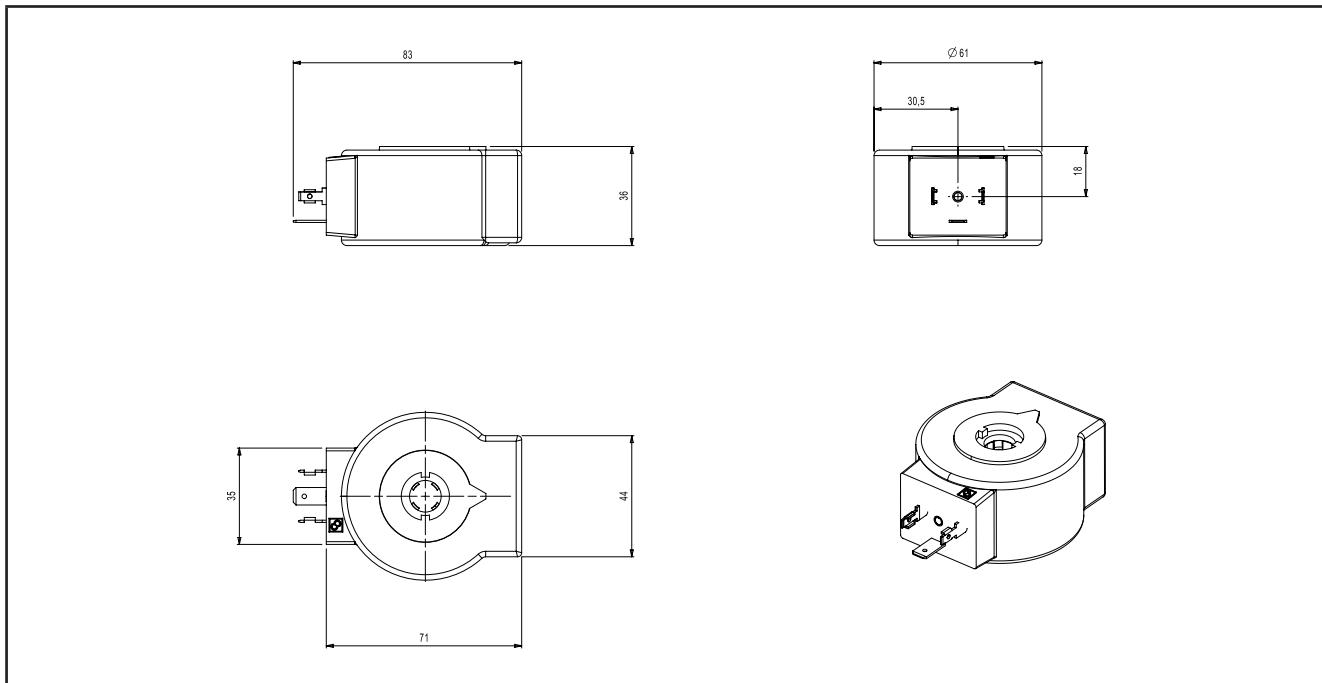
Dimensiones mecánicas bobina modelos PXVE0ARA60100, PXVS0ARA60100
